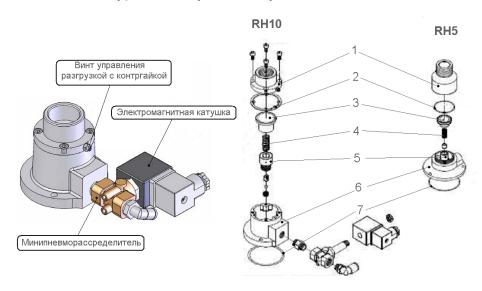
Клапаны впускные RH5 и RH10: 1 – крышка; 2 – прокладка; 3 – тарелка; 4 – пружина; 5 – направляющая тарелки; 6 - корпус; 7 – кольцо уплотнительное.
